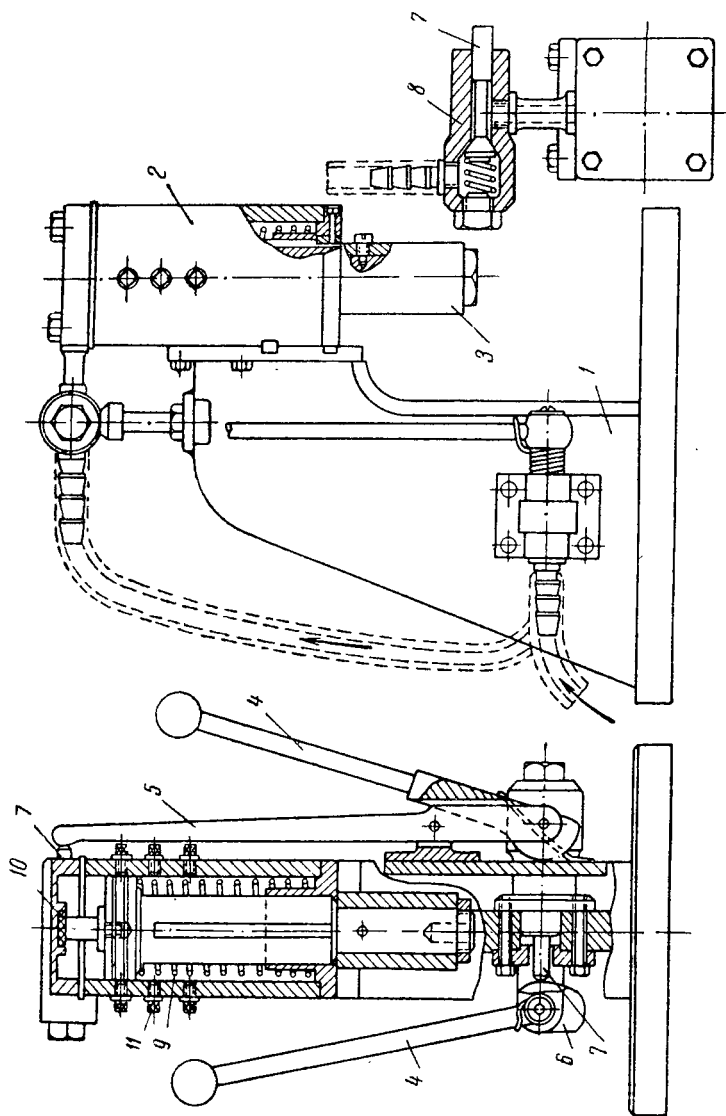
Настольный пневматический пресс для гибки и клепки петушков
